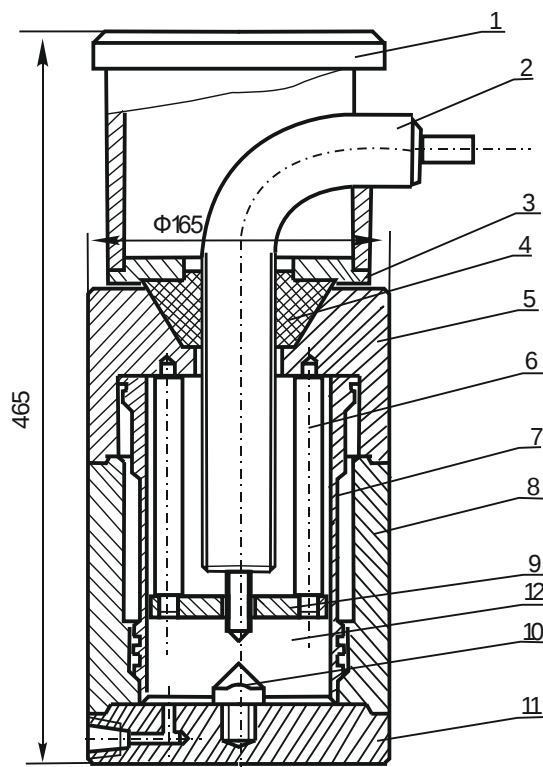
Приспособление для раздачи гильзы цилиндра двигателя ЗИЛ-5301
